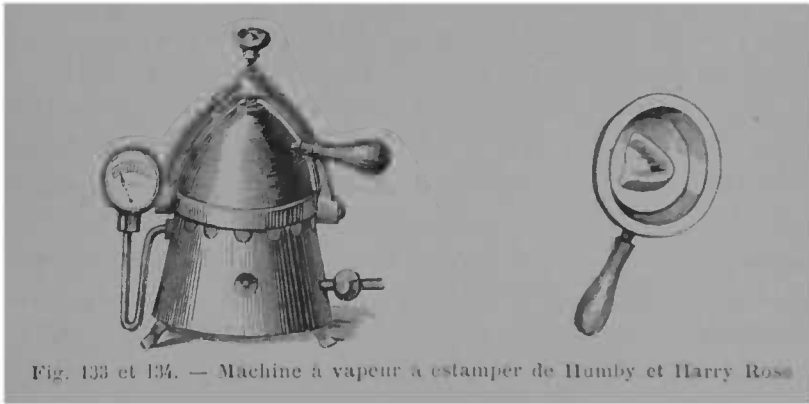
et 134. — Machine à vapeur à estamper de Humby et Harry Rose
